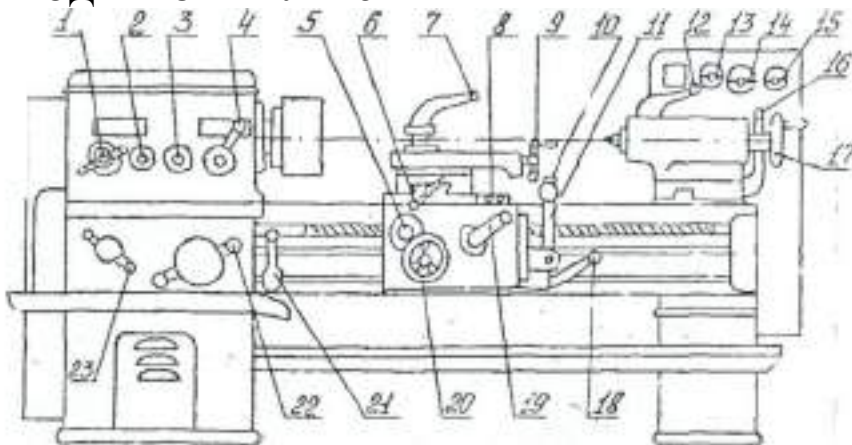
ОБЩИЙ ВИД СТАНКА
